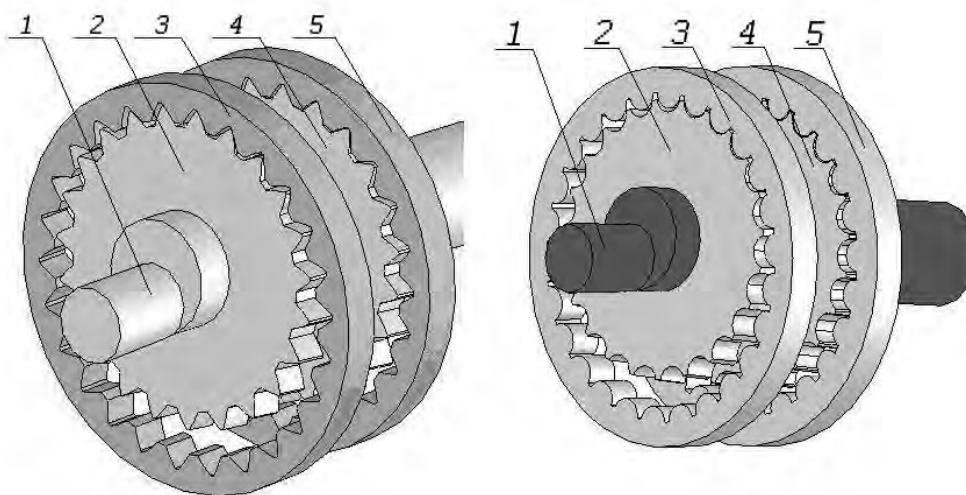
Твердотельная модель прецессионной передачи типа 2К-Н с эвольвентными и круговыми зубчатыми профилями колес: 1 - вал наклонный; 2 - сателлит первой ступени; 3 - неподвижное колесо; 4 - сателлит второй ступени; 5 - подвижное колесо
